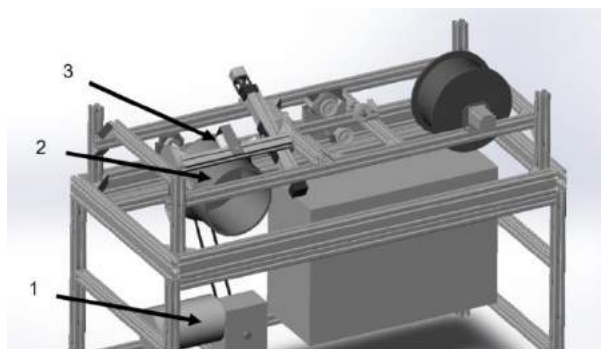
Модель станка (1 – асинхронный мотор-редуктор; 2 – бобина для создания катушки; 3 – прижимной силиконовый ролик)
